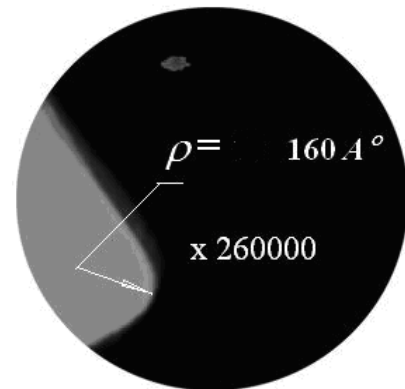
Профиль алмазного резца (вид, перпендикулярный режущей кромке)
